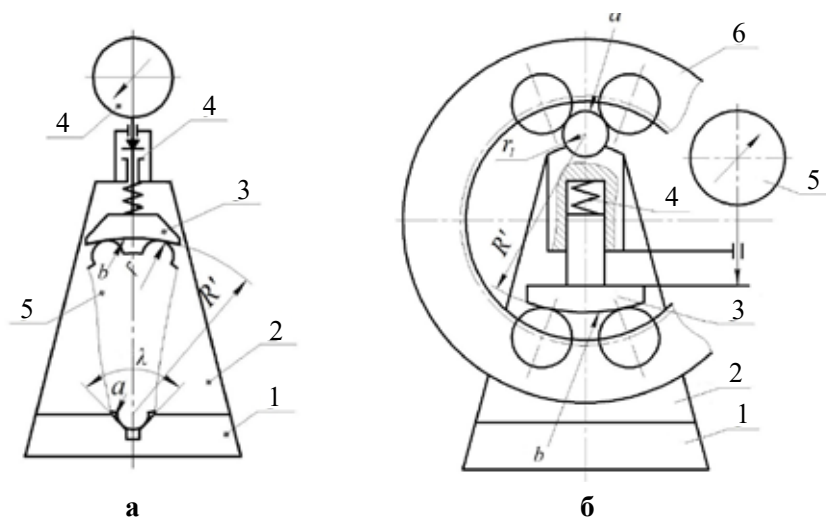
Вимірювальні пристрої контролю похибки форми внутрішнього (а) і зовнішнього (б) роторів планетарного гідромотора: 1 – стіл; 2 – стійка; 3 – вимірювальний наконечник; 4 – пружина; 5 – індикатор; 6 – контрольований ротор
